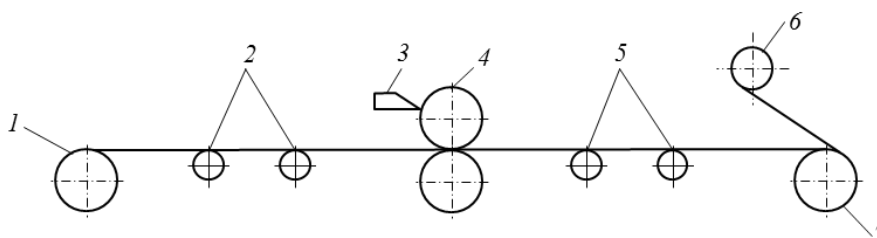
Схема изготовления пленочного связующего при помощи ракеля:
